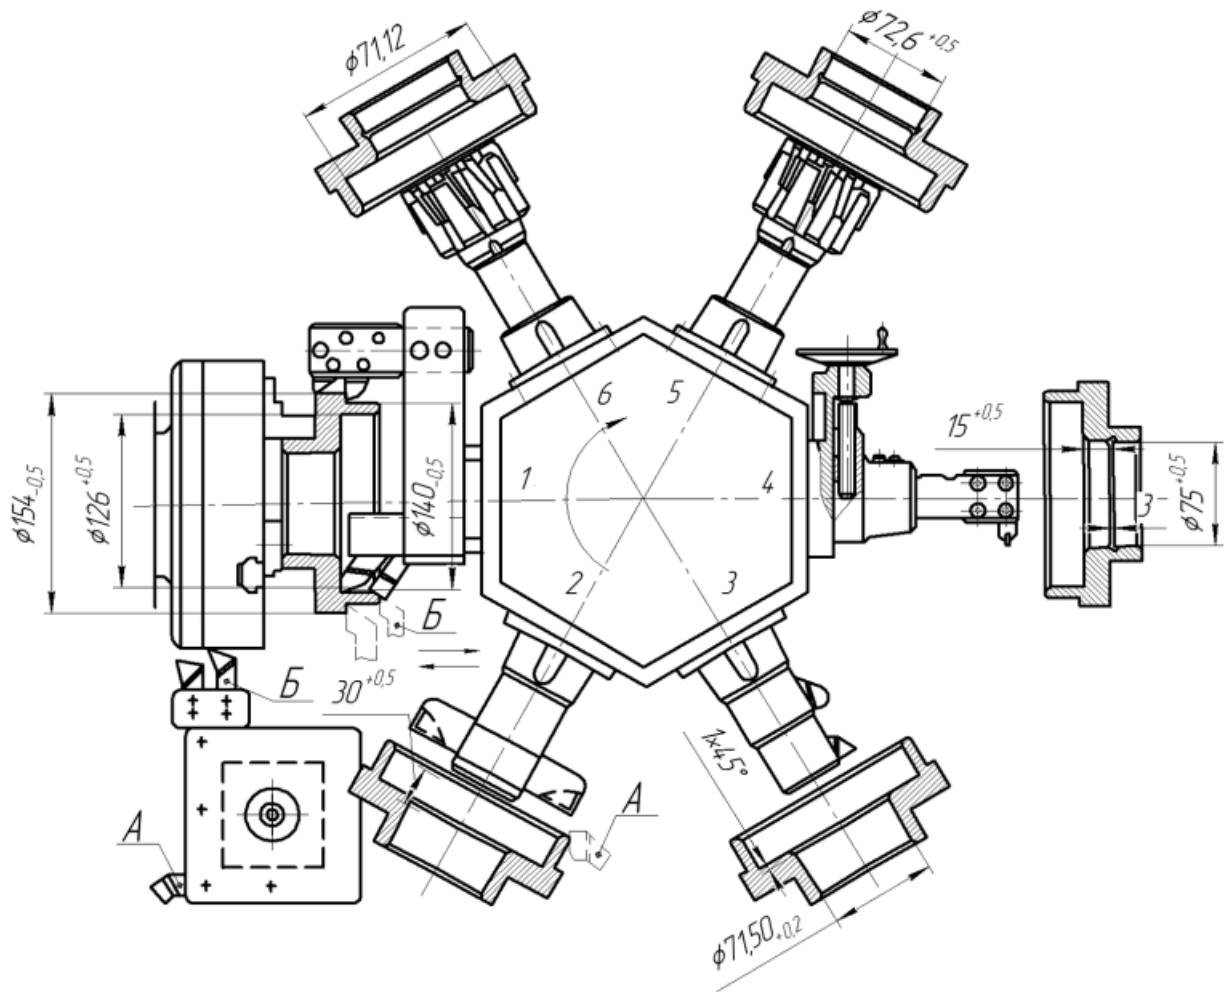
Технологічна наладка оброблення зубчастого колеса на токарноревольверному верстаті
